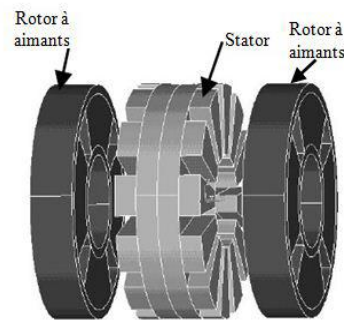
Descriptif de la machine à flux axial stator interne.[14]
